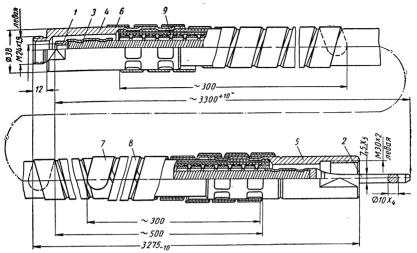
Комплектная передача типа В-122: 1, 2 — наконечники гибкого вала; 3 — гибкий вал; 4, 5 — муфты брони; 6, 7, 8 — усилительные пружины; 9 — броня
